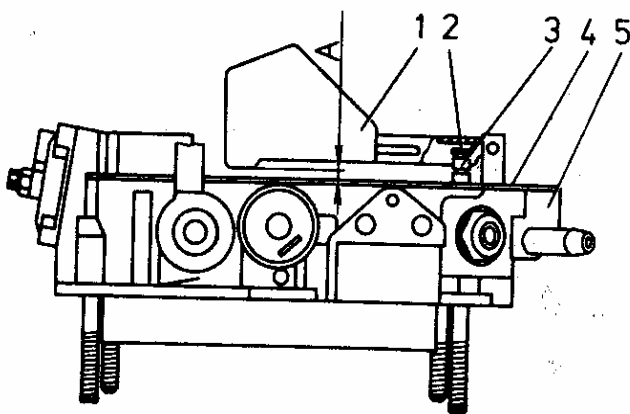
Instalación del nivel del combustible en el carburador "Solex": 1 - flotador; 2- lengüeta; 3- válvula de aguja; 4 junta; 5- tapa del carburador
